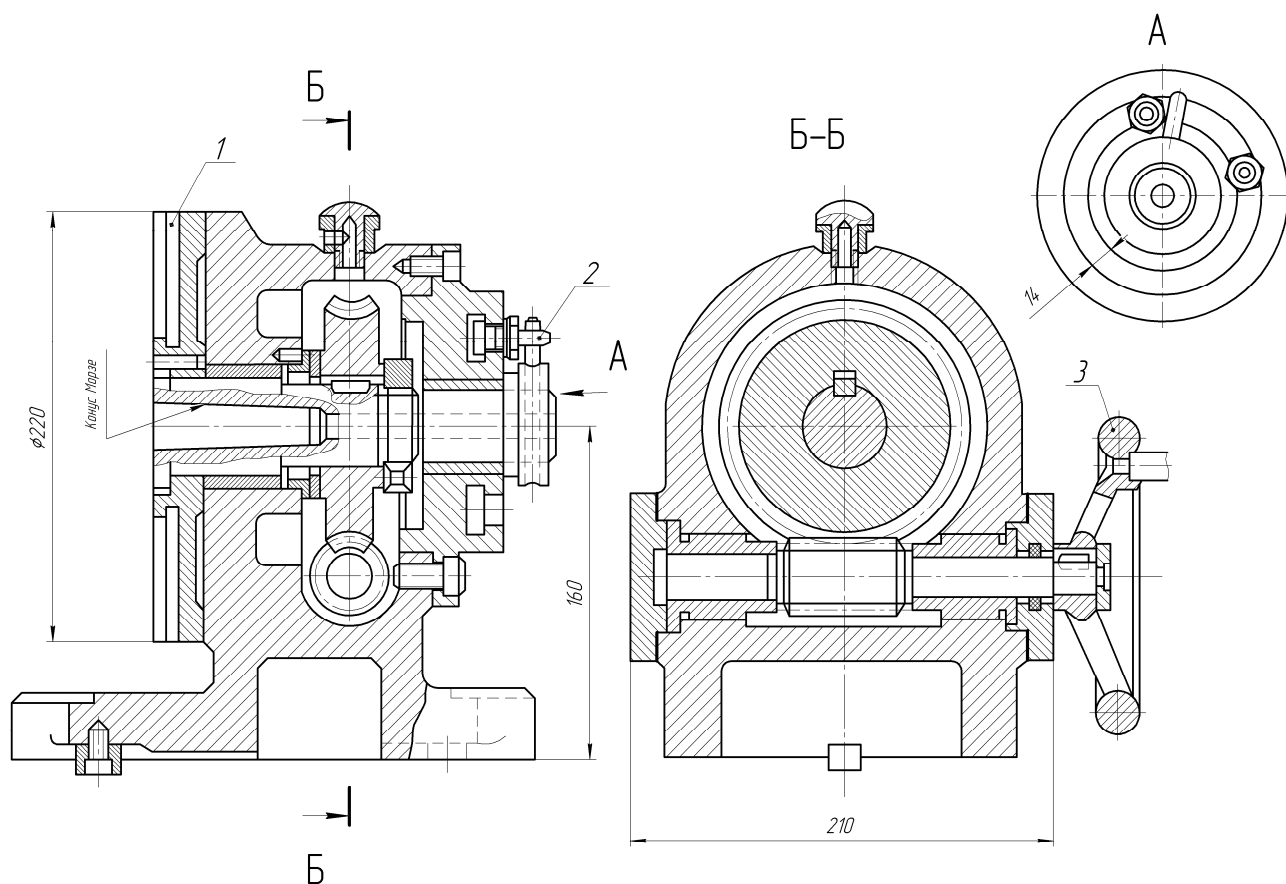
Будова й параметри стола поворотного для радіального фрезерування фасок, байонетних пазів: 1 – поворотна частина стола; 2 – рухомий упор; 3 – маховичок
